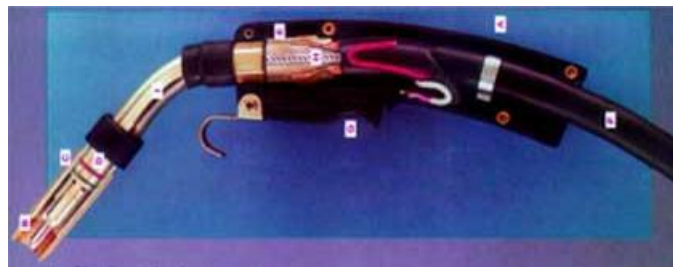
a) Pistola para soldadura metálica con arco eléctrico y gas.
